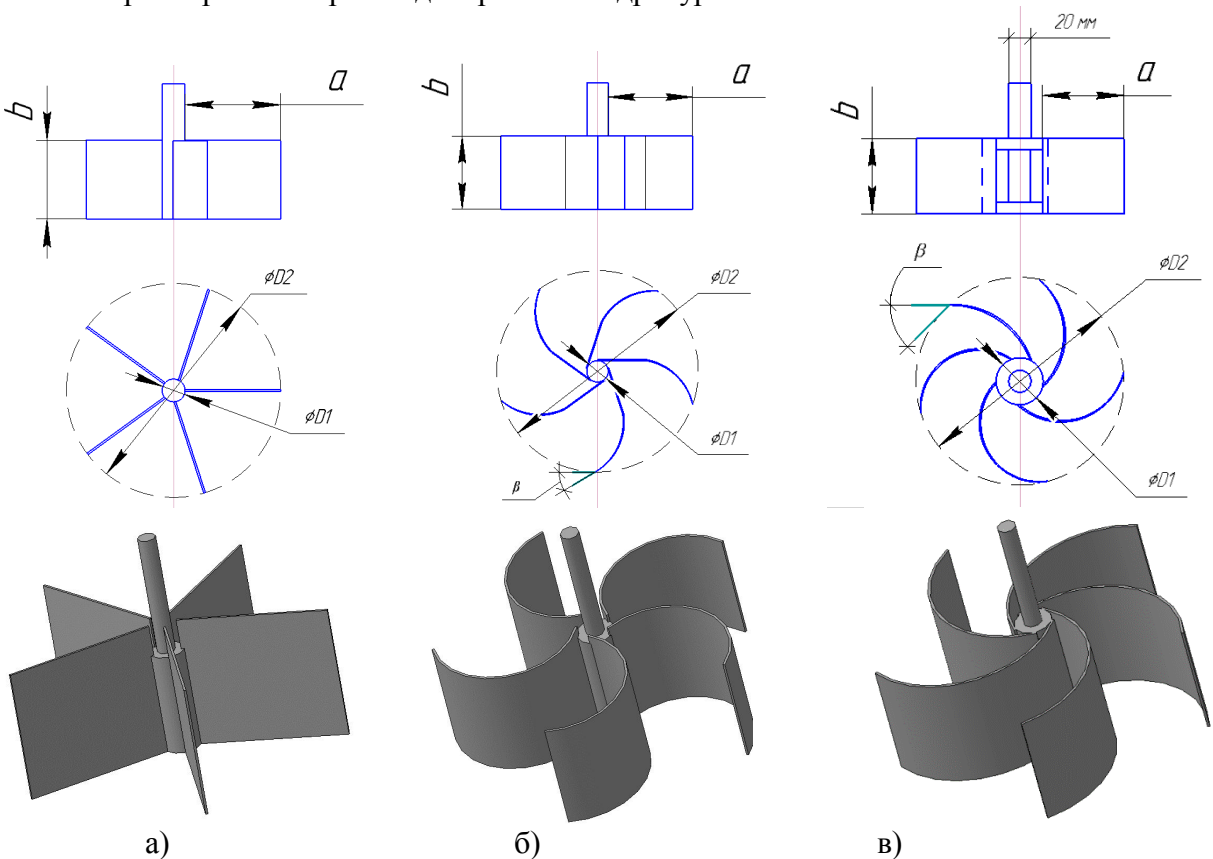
Чертеж и 3D модель осевой водоворотной гидротурбины: а) плоской лопастью; б) цилиндрической лопастью; в) цилиндрической лопастью с зазором
